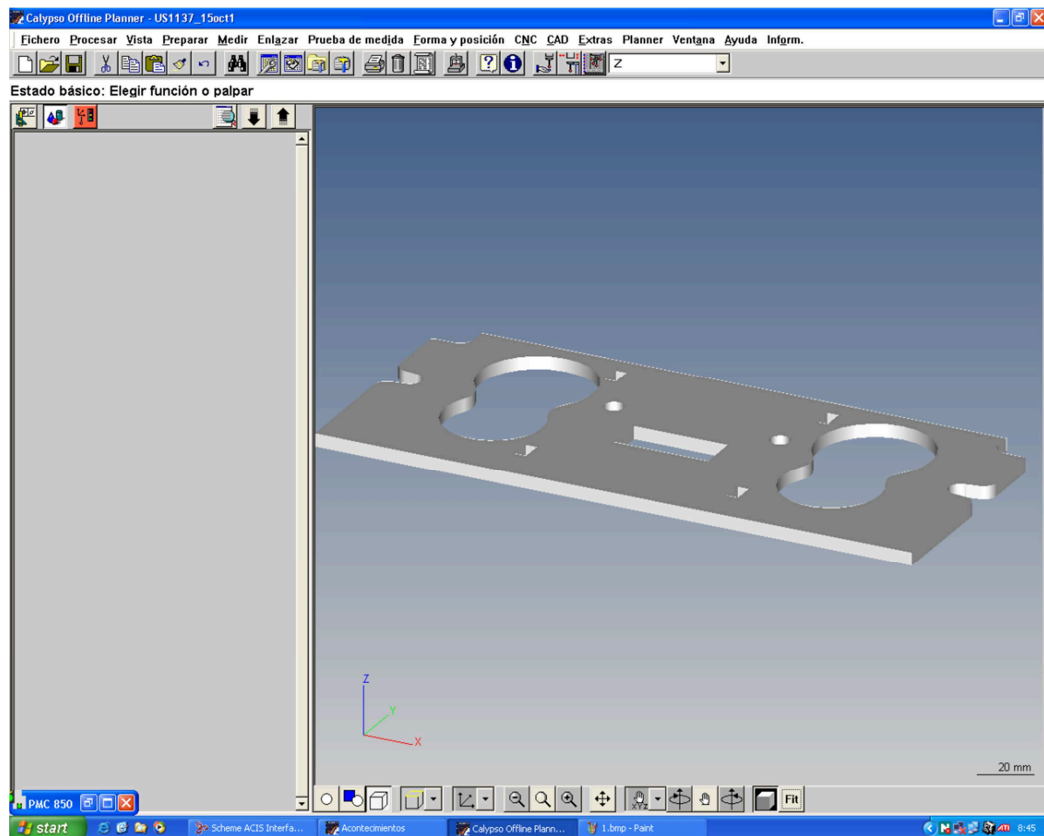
Anexo IV. Pieza CAD importada en Calypso.
